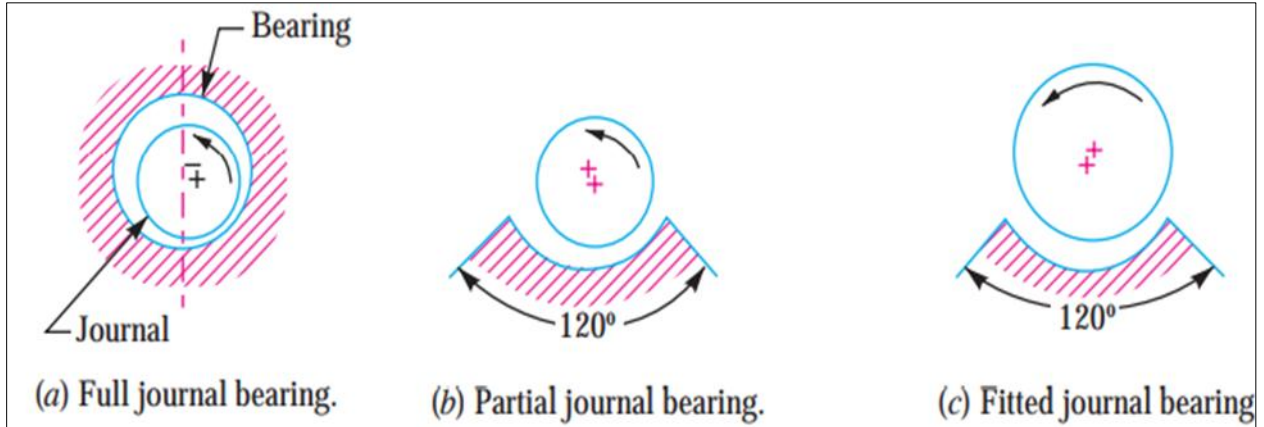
जर्नल किंवा स्लीव्ह बेअरिंग (Journal or sleeve bearing)
